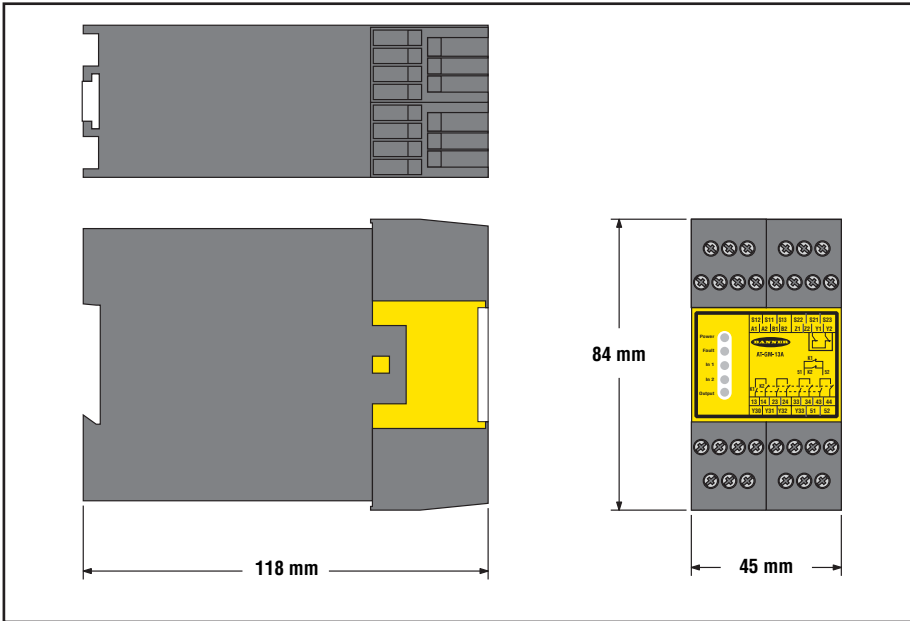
Dimensioni del modulo di sicurezza DUO-TOUCH SG
